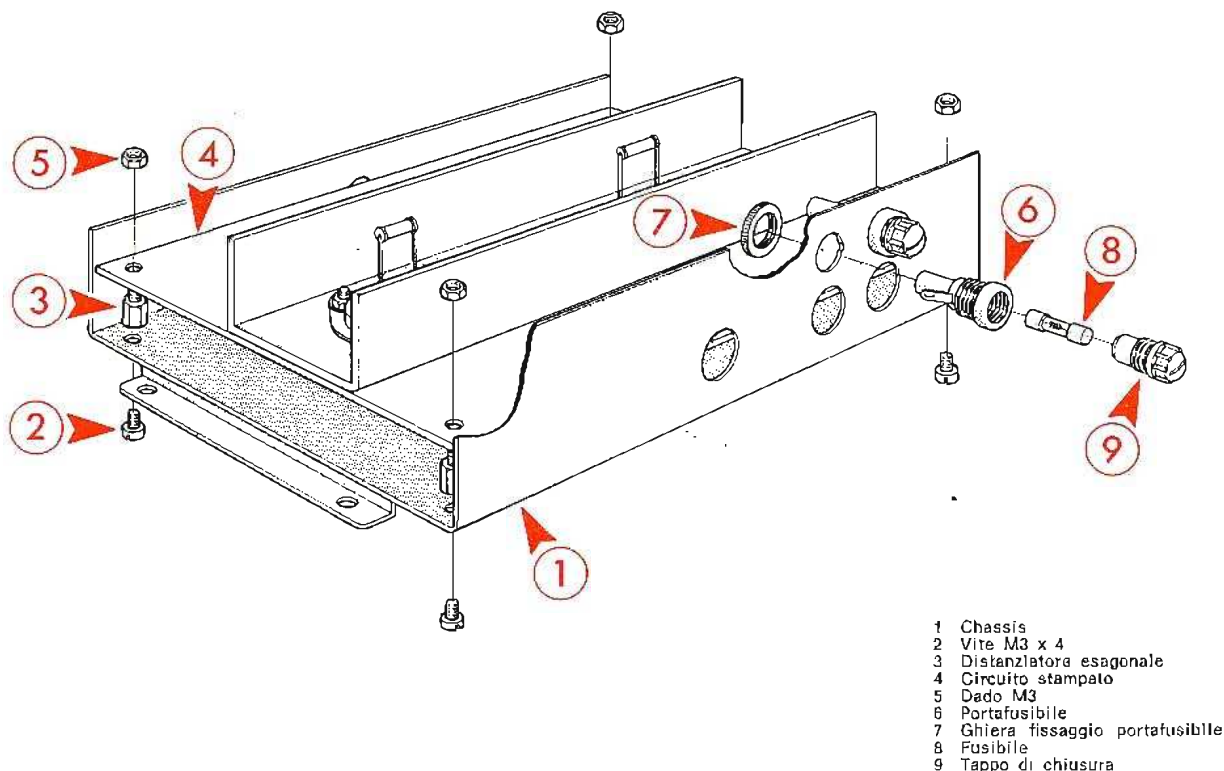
Montaggio di alcuni componenti sullo chassis.
